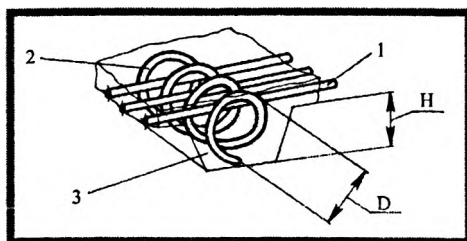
Зубчатый ремень со спиральными цилиндрическими пружинами:
